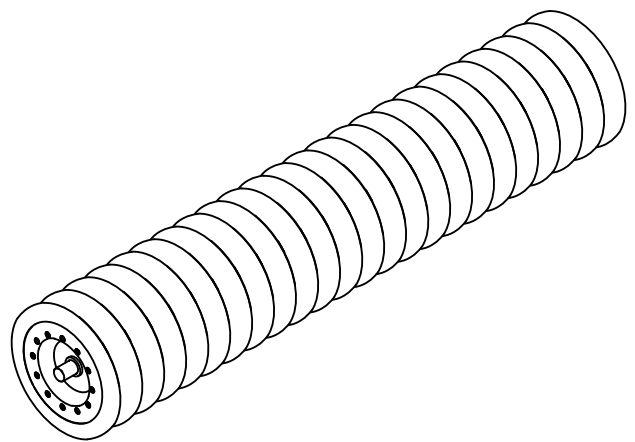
System CrossBoard Heavy (Carrier 420–650)
